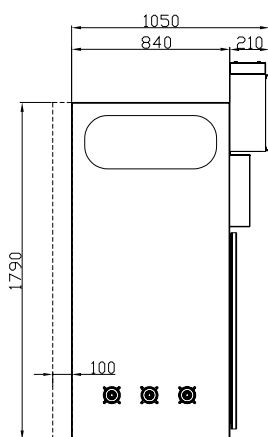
Габаритные размеры КСО с шириной корпуса 650 мм
